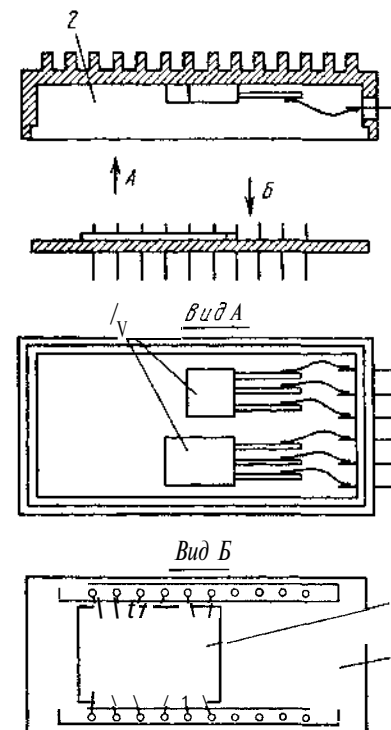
Конструкция микросборки стабилизатора напряжения
